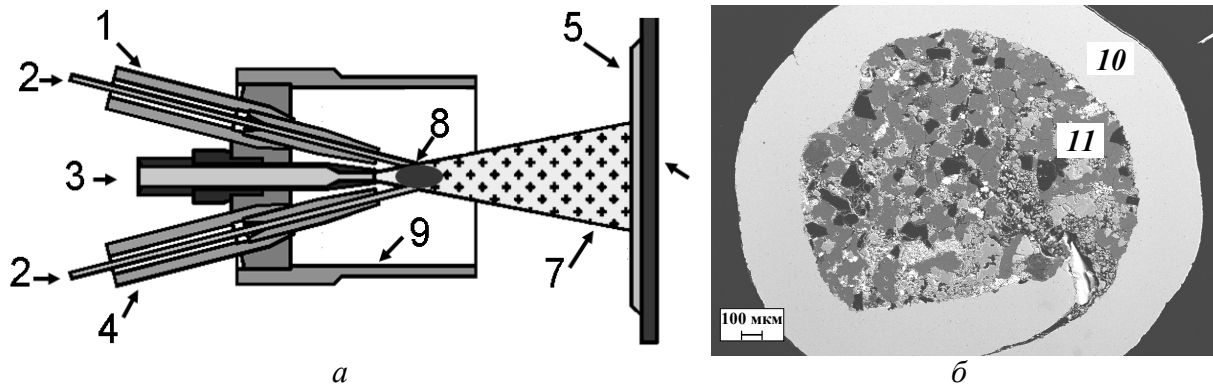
Типова схема металізатора для ЕДН покриттів (а) та поперечний переріз ПД (б): 1 – катод; 2 – ПД; 3 – стиснене повітря; 4 – анод; 5 – покриття; 6 – підложка; 7 – розплавлений метал; 8 – дуга; 9 – захисний кожух; 10 – оболонка; 11 – шихта.
